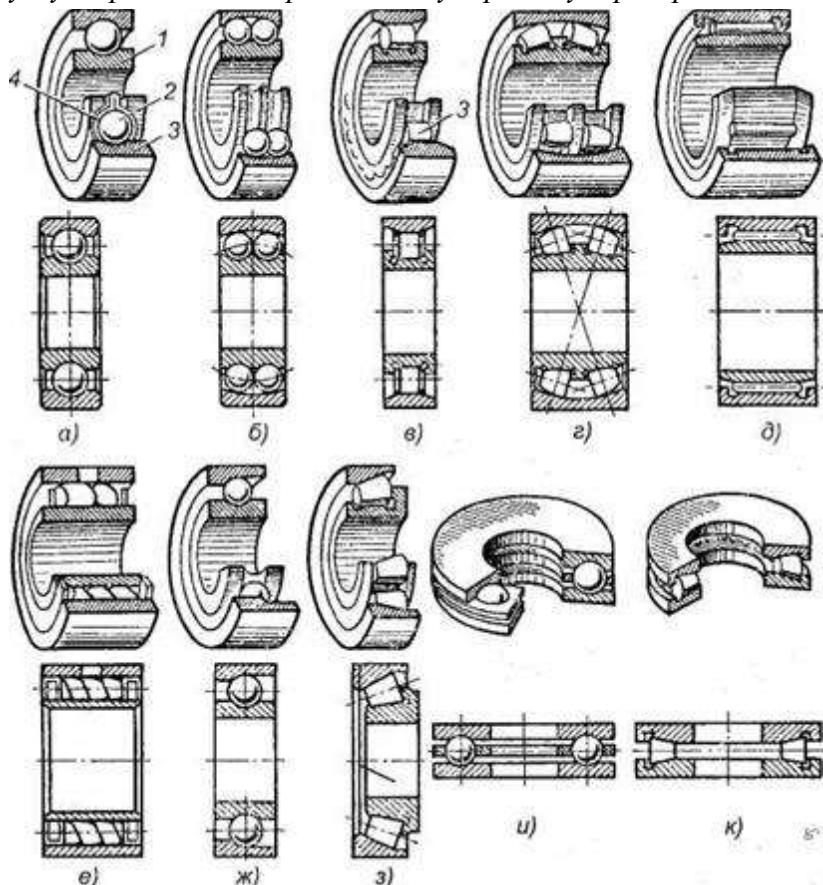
Подшипники качения: а, б, в, г, д, е — радиальные подшипники; жс, з — радиально-упорные подшипники; и, к — упорные подшипники; 1 — внутреннее кольцо; 2 — тело качения; 3 — наружное кольцо; 4 — сепаратор.
